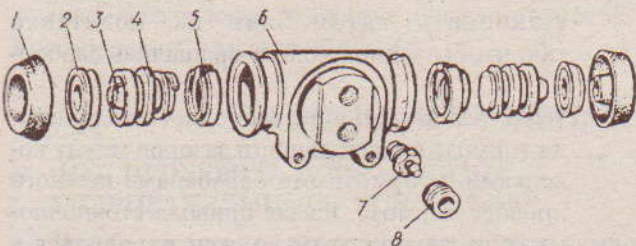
Детали колесного цилиндра тормоза: 1 - колпак защитный; 2 - манжета поршня; 3 - стержень опорный; 4 - поршень; 5 - кольцо поршня; 6 - цилиндр; 7 - клапан выпуска воздуха; 8 - колпачок клапана предохранительный
